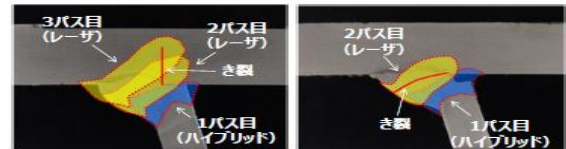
LAHWの施工手順(1パス~3パス施工)とき裂溶融位置
